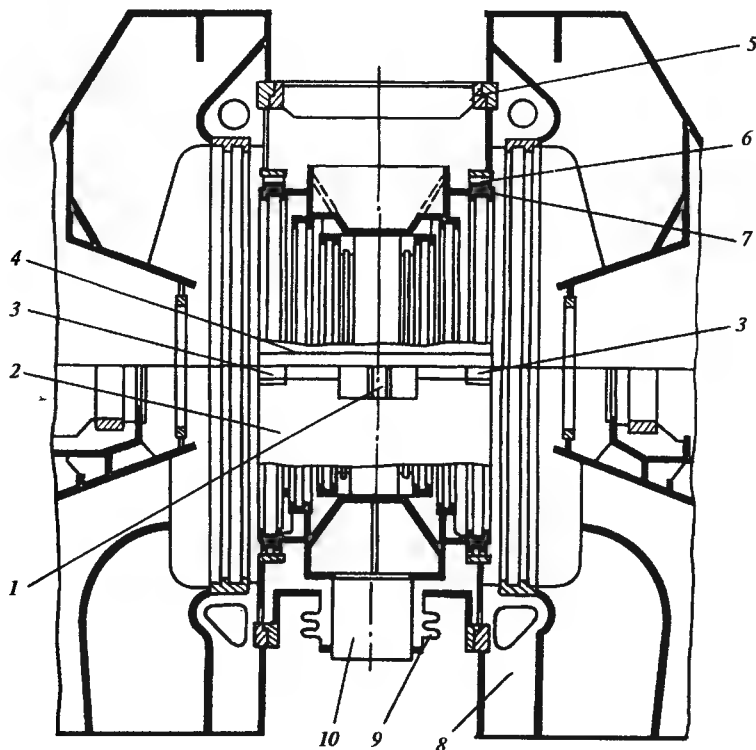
Конструктивная схема двухстенного корпуса ЦНД:
